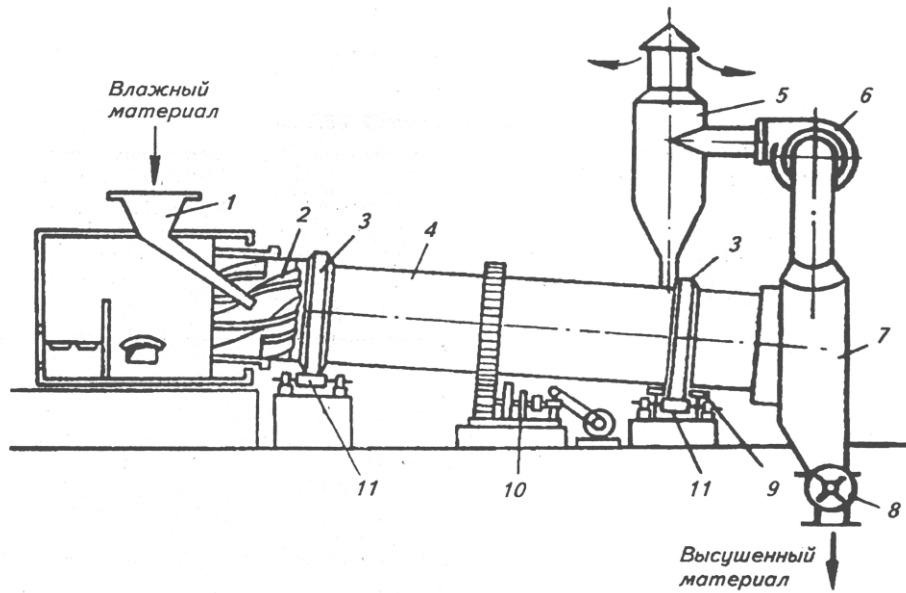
Схема барабанной проточной сушилки: 1 – загрузочное устройство; 2 – перемешивающие лопасти; 3 – опорный бандаж; 4 – барабан; 5 – циклон; 6 – вентилятор; 7 – разгрузочное устройство; 8 – шлюзовый затвор; 9 – нижняя опора; 10 – зубчатая передача; 11 – опорные ролики
